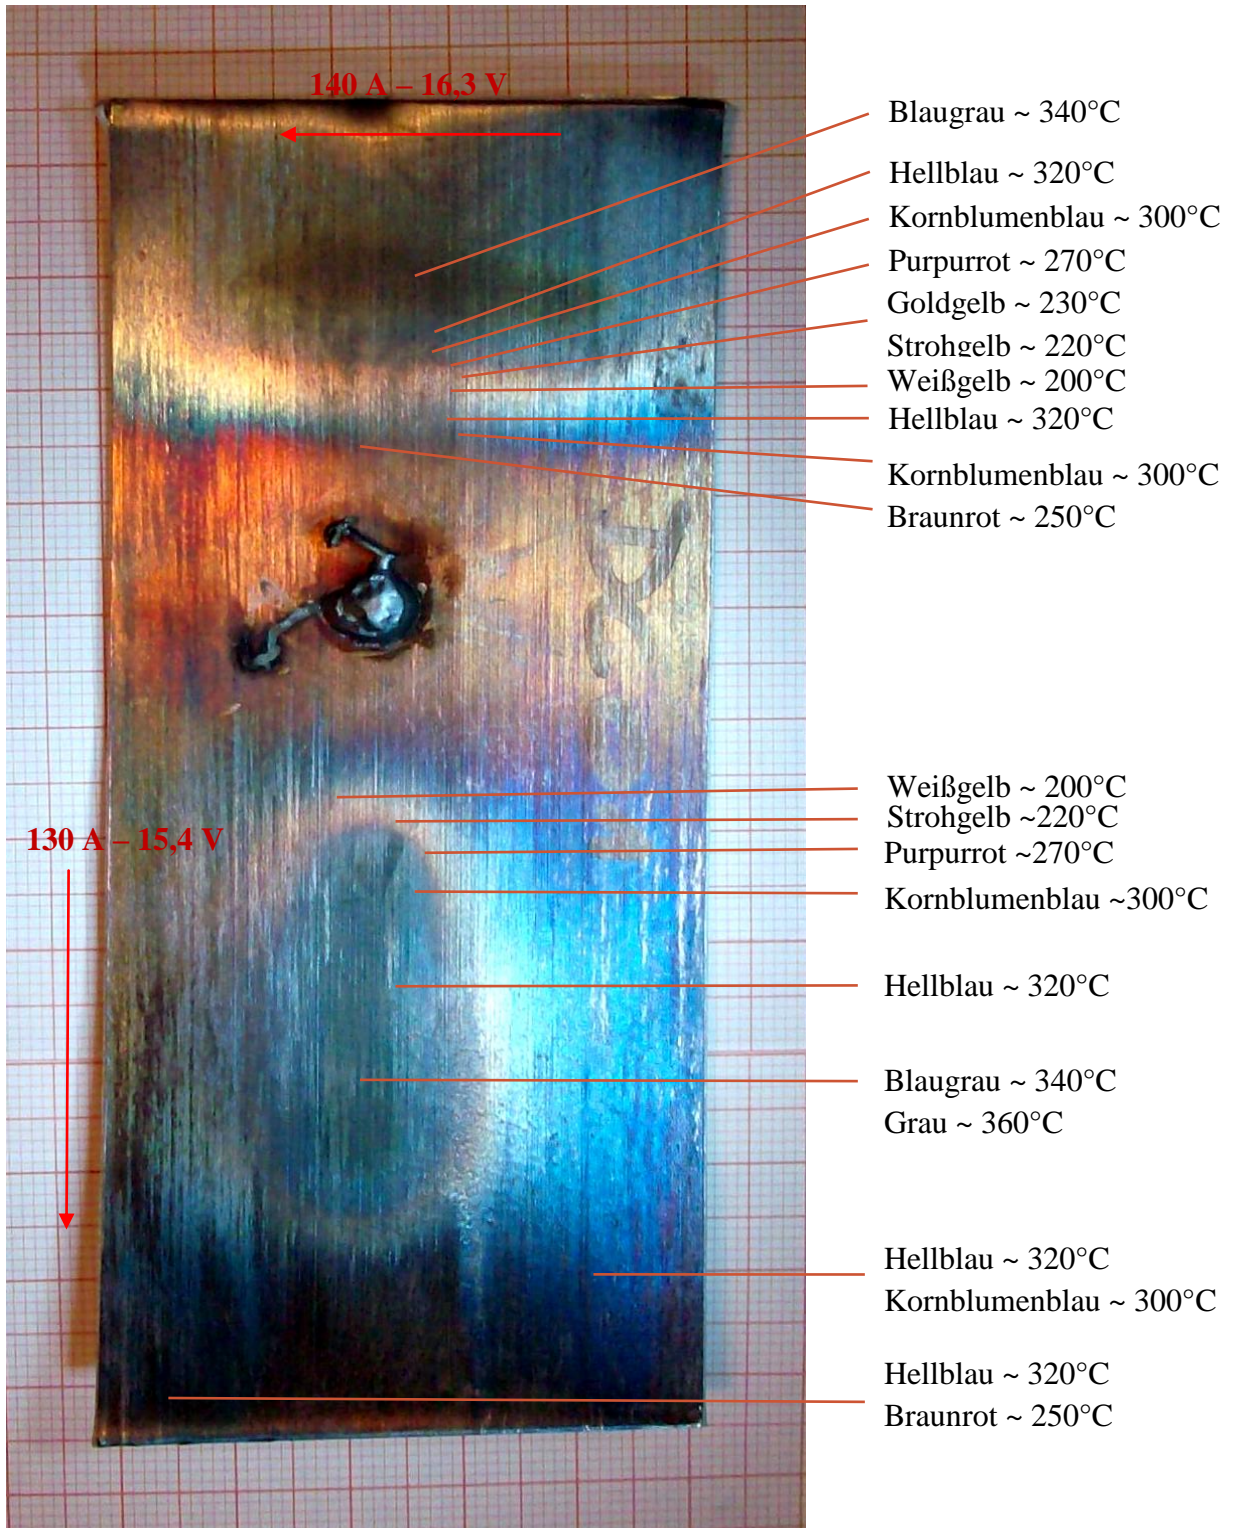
Anlassfarben der Auftragsschweißung
